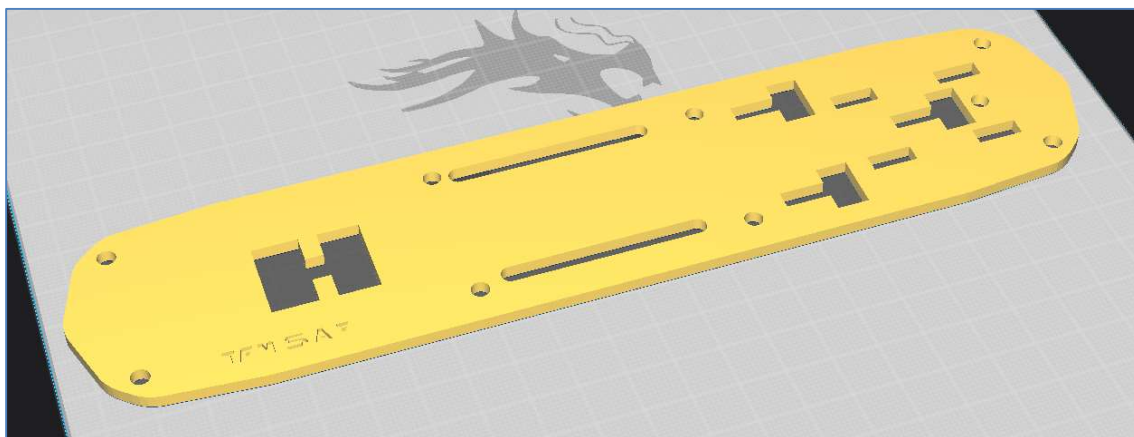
Colocación de la cubierta sobre la placa de impresión.
